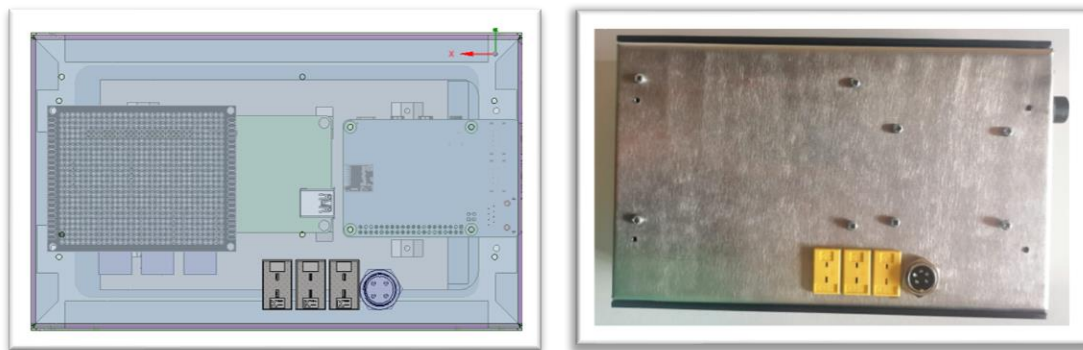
Diseño y montaje de la caja del módulo parte posterior
